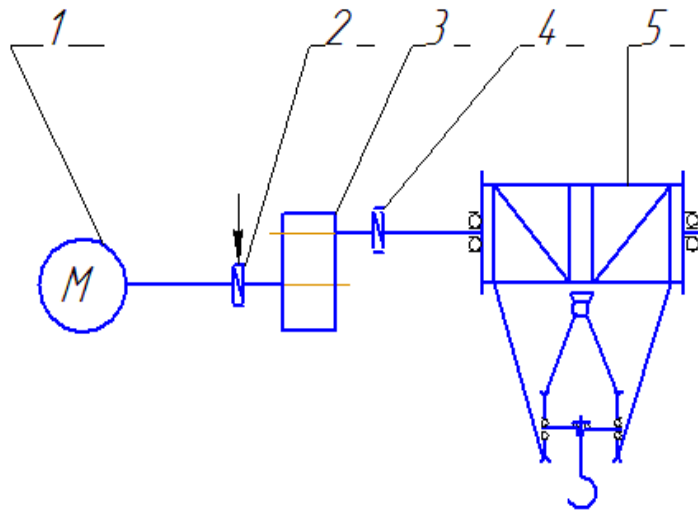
Схема механізму підйому 1 – електродвигун; 2 – муфта з гальмівним шківом; 3 – редуктор; 4 – муфта; 5 – барабан
